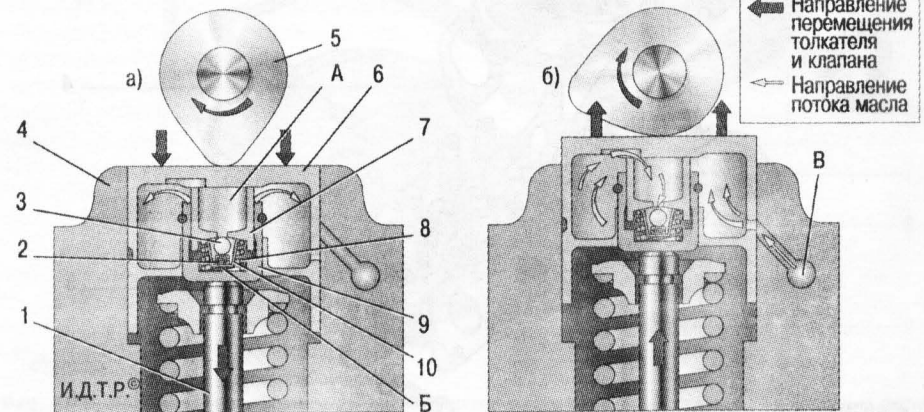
Схема работы гидрокомпенсатора зазора в клапанном механизме: а – открытие клапана; б – закрытие клапана; 1 – клапан; 2 – пружина обратного клапана; 3 – обратный клапан; 4 – головка блока цилиндров; 5 – кулачок распределительного вала; 6 – толкатель; 7 – плунжер; 8 – пружина плунжера; 9 – гильза; 10 – корпус обратного клапана; А, Б – полости гидрокомпенсатора; В – масляный канал
